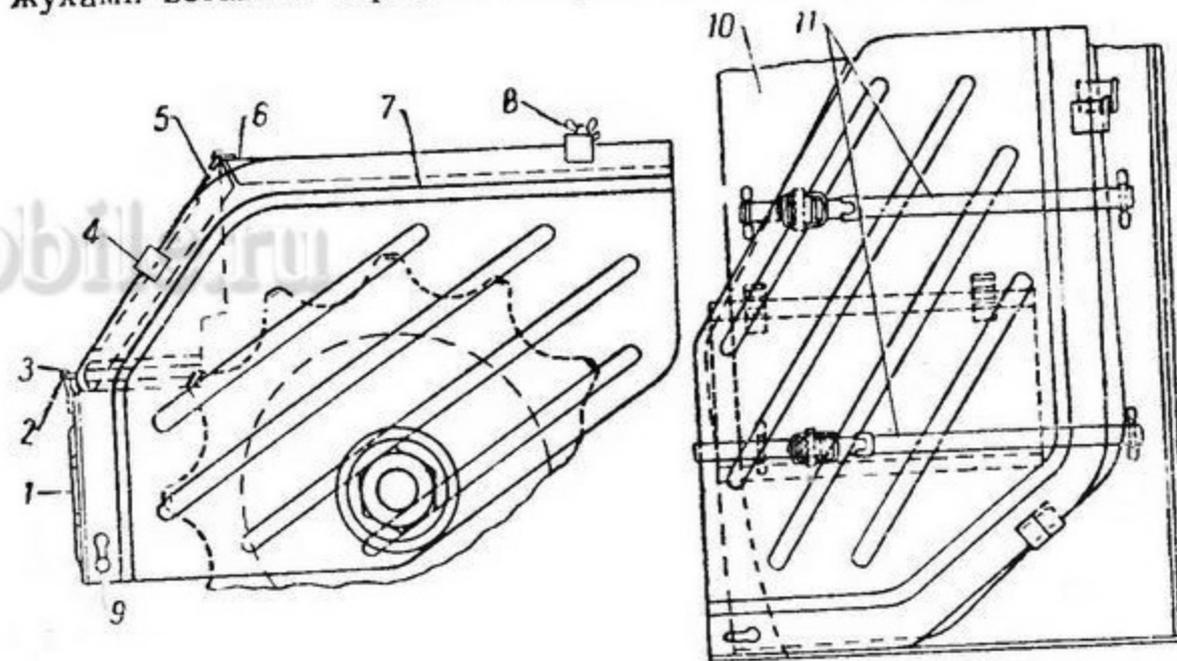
Установка и укладка гидродинамических кожухов. 1—передний кожух, 2—петля, 3—скоба, 4—центрирующий кронштейн, 5—брызговик, 6—крыло, 7—боковой кожух, 8—болт-барашек, 9—палец, 10—стенки воздухоотвода, 11—ремни. Слева—установка кожухов, справа—укладка.
